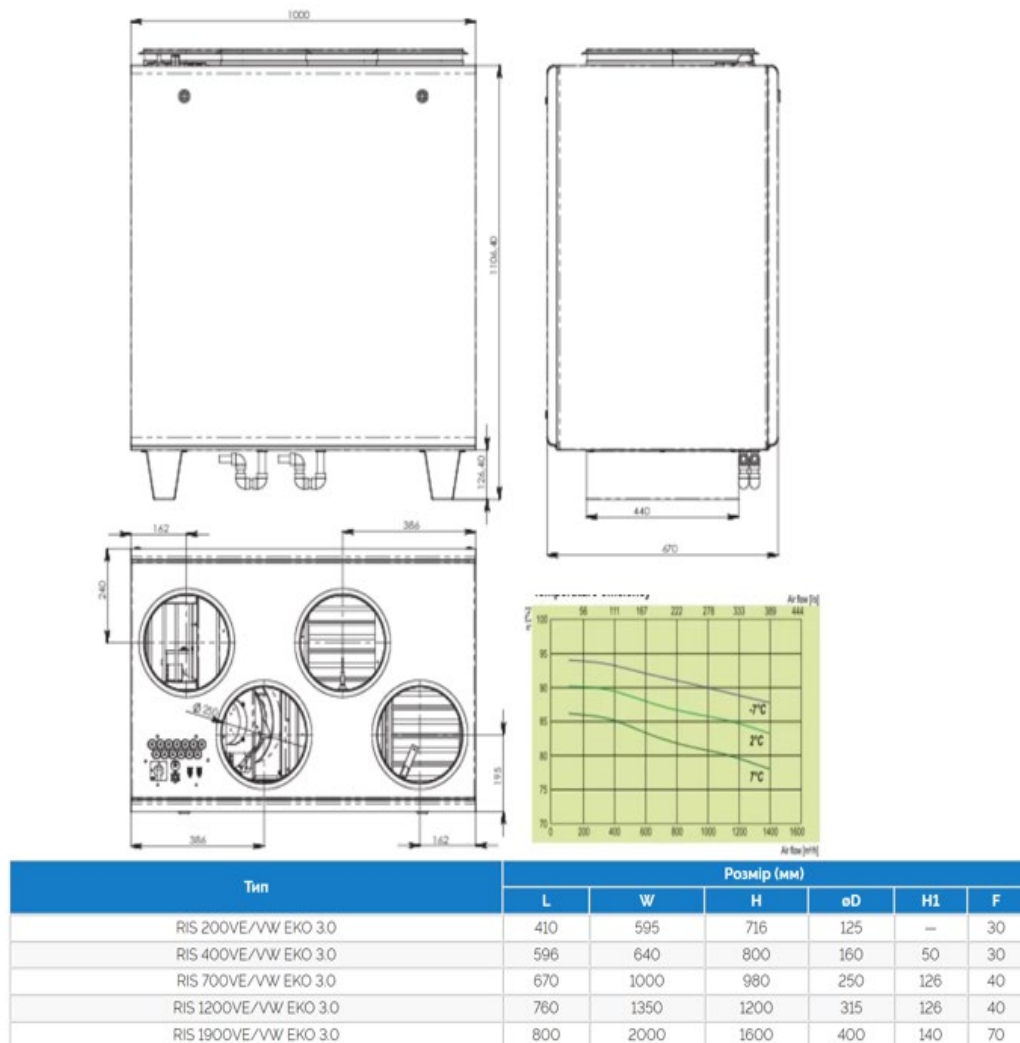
Типорозміри припливно-витяжної установка SALDA RIS 700 VE EKO 3.0 [16]
